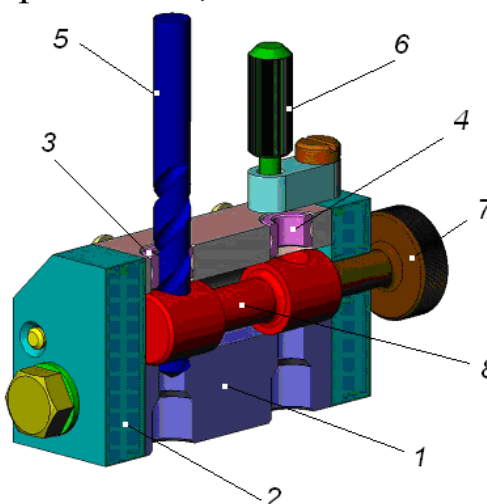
Продольный разрез кондуктора: 1 – ложемент; 2 – фланец; 3 – крышка; 4 – направляющая втулка; 5 – сверло (развертка); 6 – прижим; 7 – осевой прижим; 8 – образец
